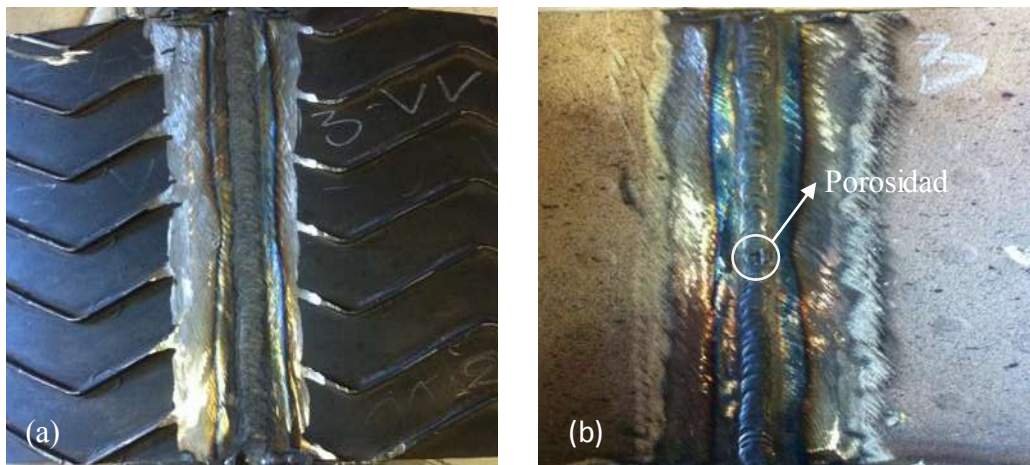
Cara de la soldadura y pasada de raíz en la unión soldada tipo B.
